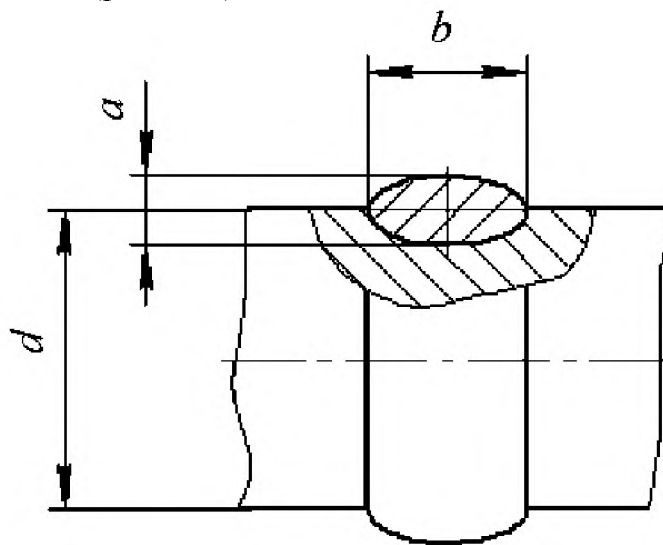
Схема шийки деталі з наплавленим валиком матеріалу
